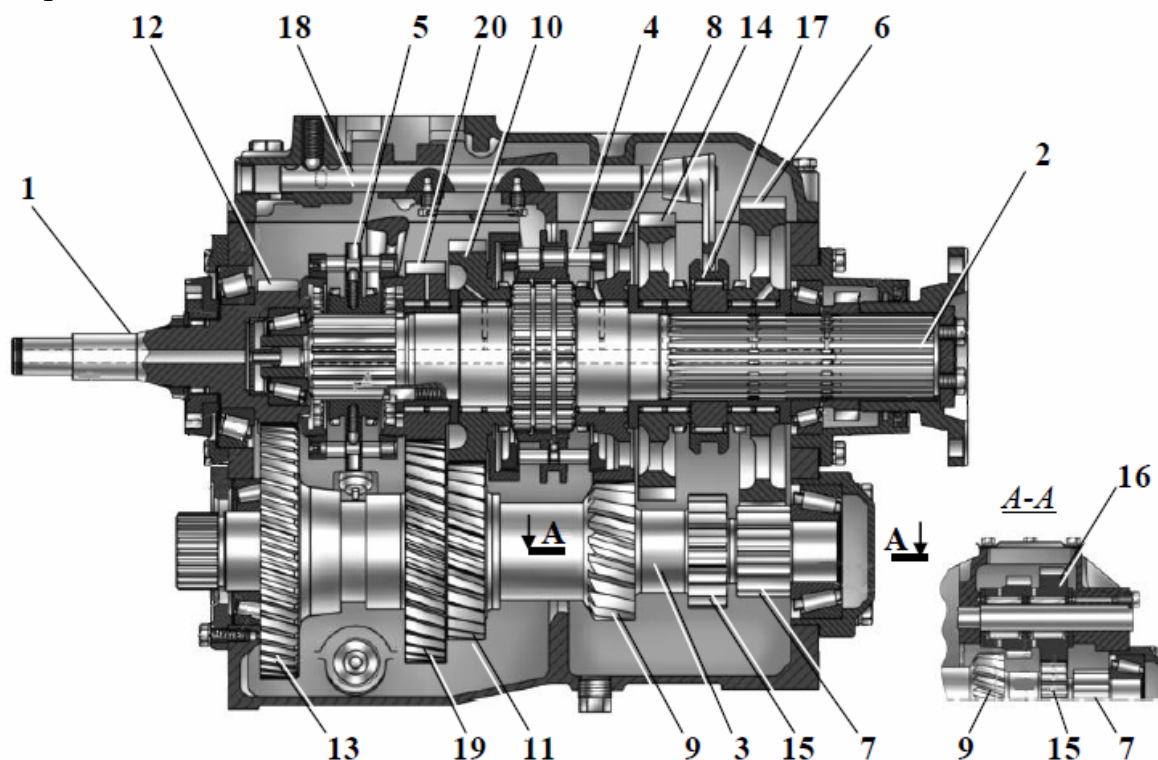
Конструкция основной трехвальной пятиступенчатой коробки передач КАМАЗ модели 154:
